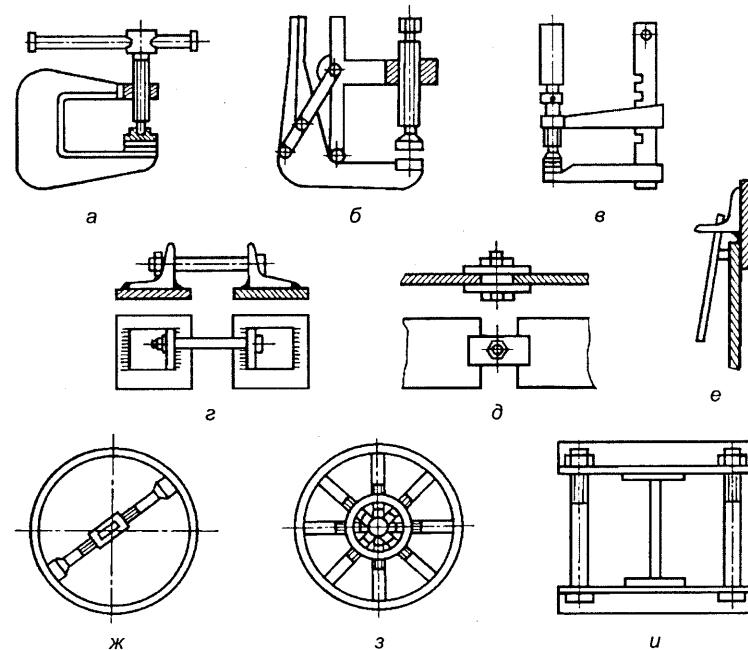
Переносные универсальные приспособления для сборки: а, б, в – струбцины; г, д – стяжные устройства; е – прижим рычажный; ж, з – распорки (стяжки) винтовые; и – стяжное приспособление (хомут)
